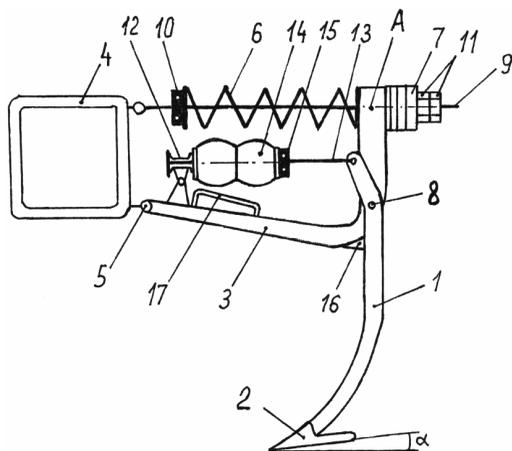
Принципиальная схема предлагаемого рабочего органа почвообрабатывающей машины в заглубленном рабочем положении
